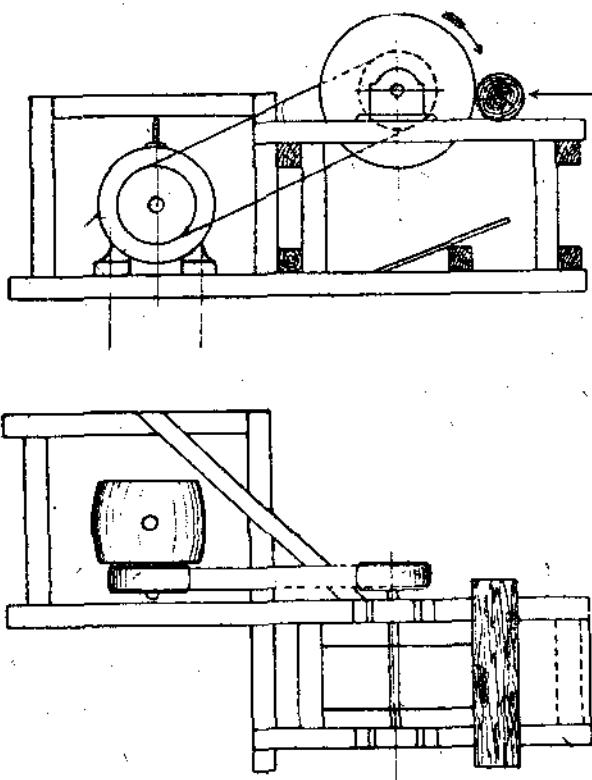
Дровопильный станок с двумя пилами в ручной подачей.
